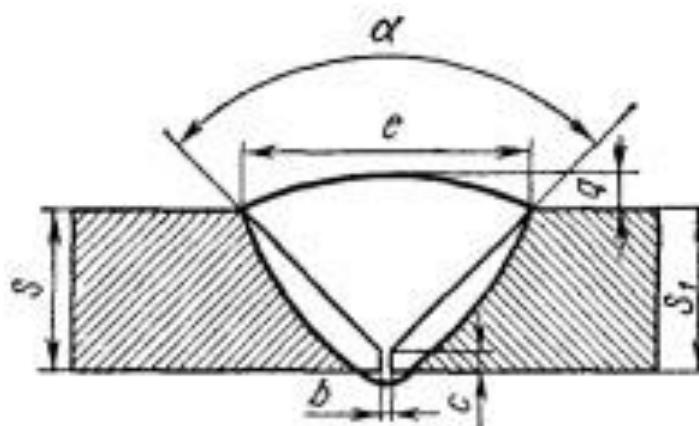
Поперечное сечение сварного соединения с разделкой кромок
